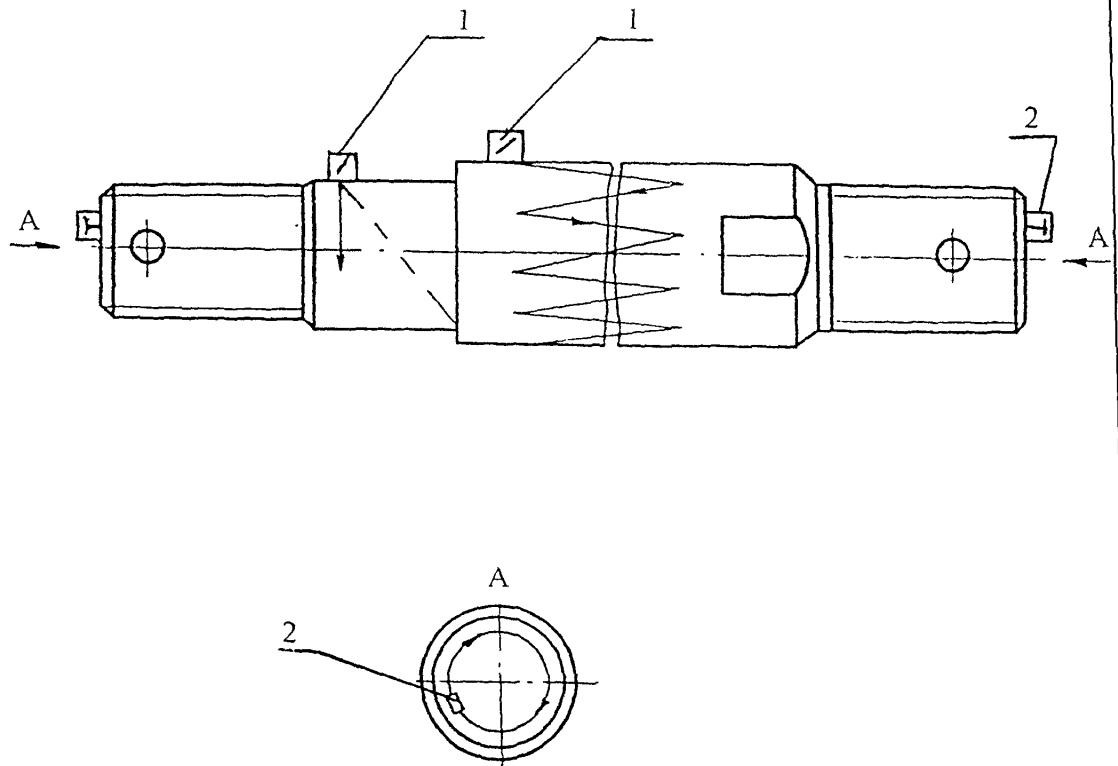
Схема контроля подвески ПБК4 - 01.05.006
